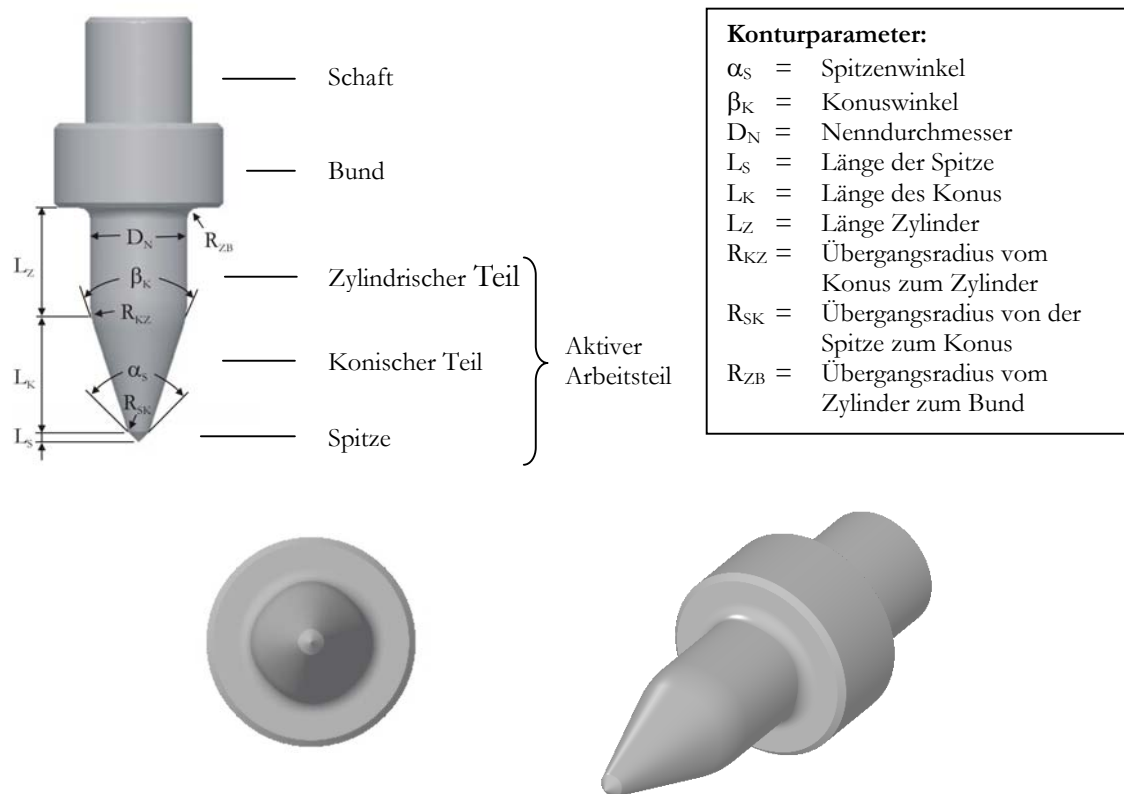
Geometrie des Werkzeuges zum Thermoflößlochformen
